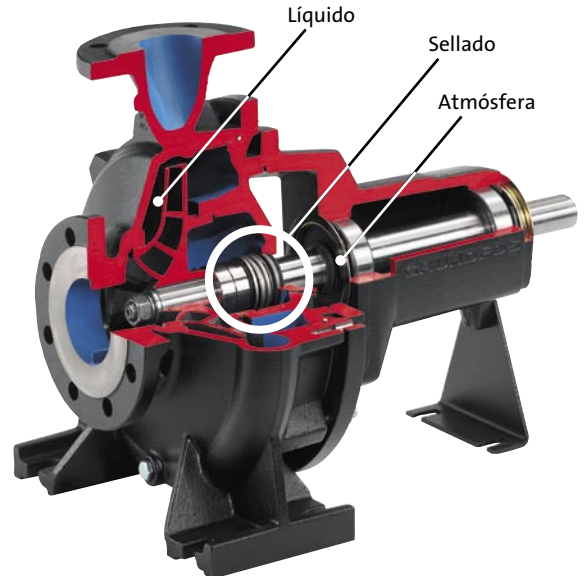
Ejemplo de bomba estándar con cierre mecánico
